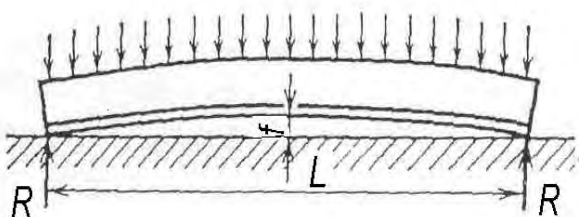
Продольная деформация сварной балки и схема ее нагружения
